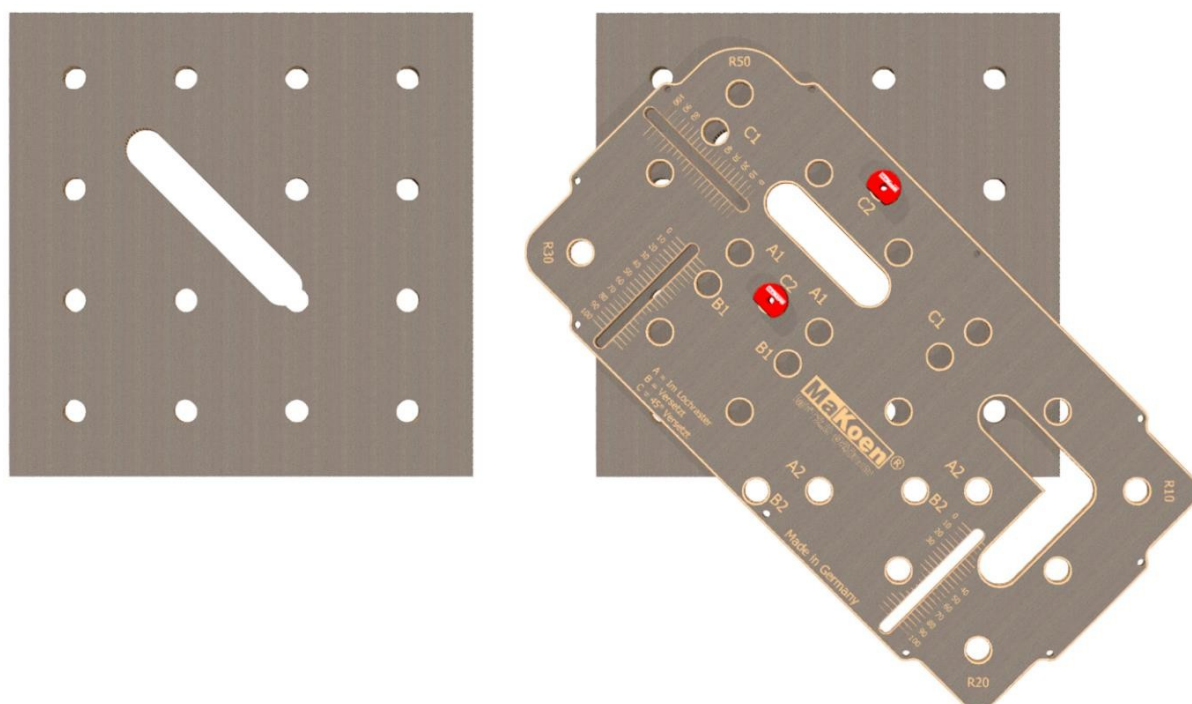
Schuine langgat door toepassing van opstelling B2
